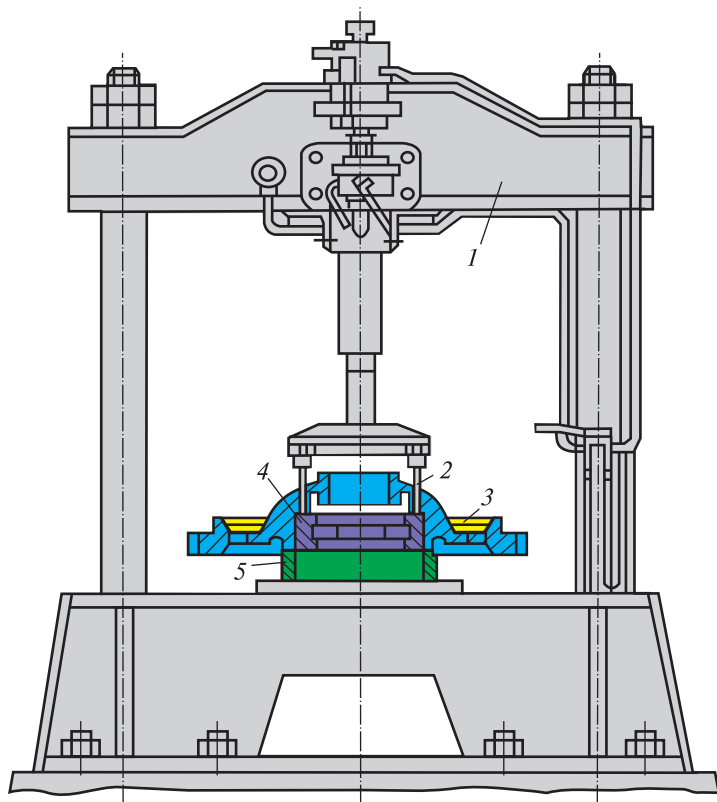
Гидравлический пресс для выпрессовки подшипника из щита:
